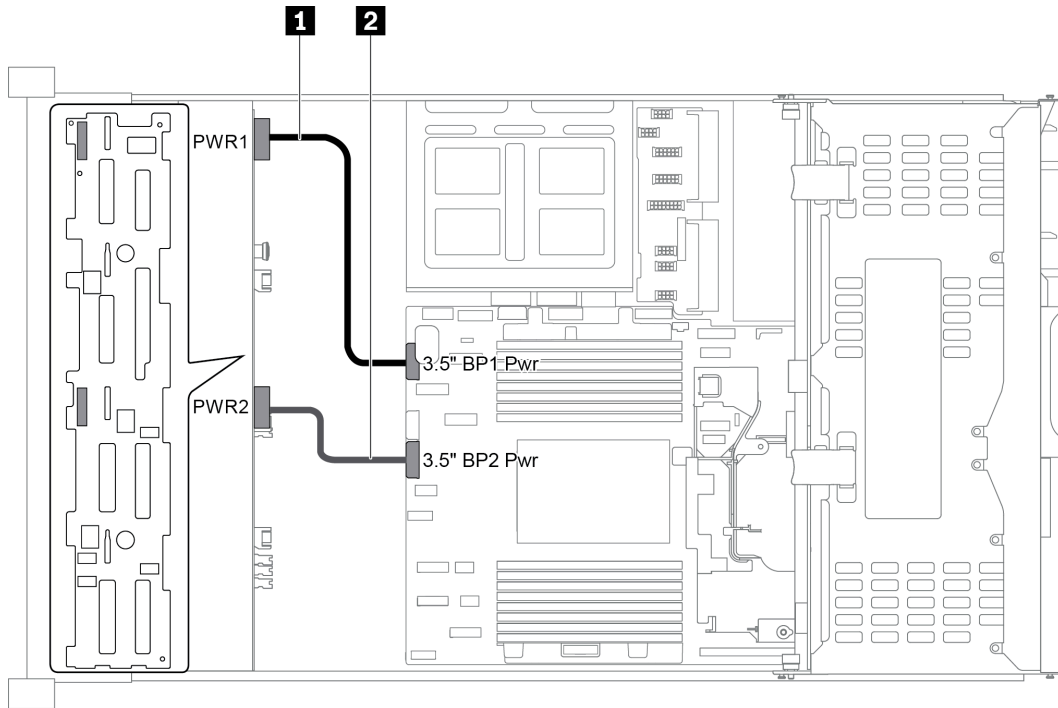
Câblage d'alimentation pour les fonds de panier d'unité avant 3,5 pouces
